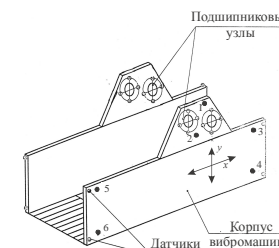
Схема расположения датчиков на корпусе выбивной машины и способы их крепления
